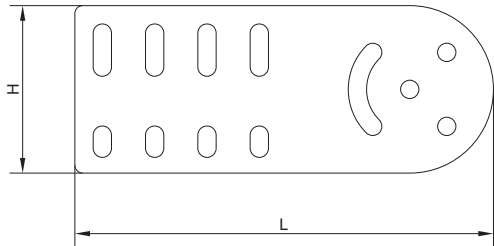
Пластина шарнирного соединения / Figure D.2 — CLM50D-PSH, EALM50D-PSH Hinge joint plate
